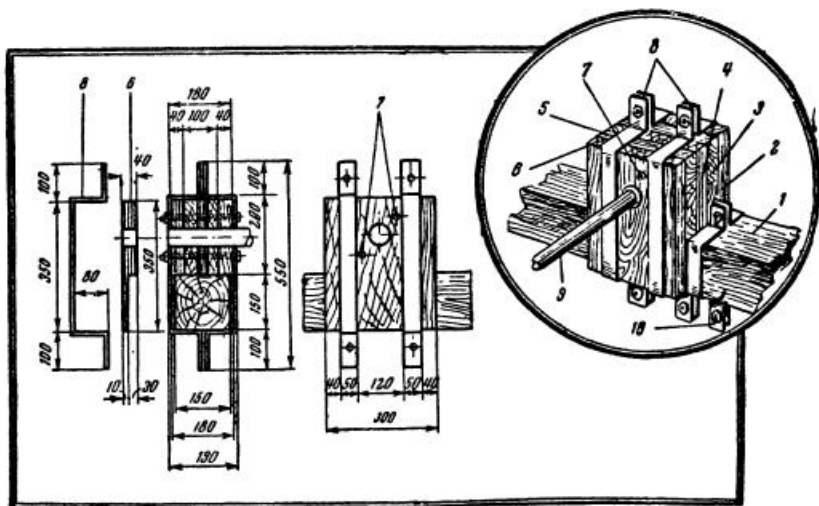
Самодельный деревянный подшипник для гидроротора:
